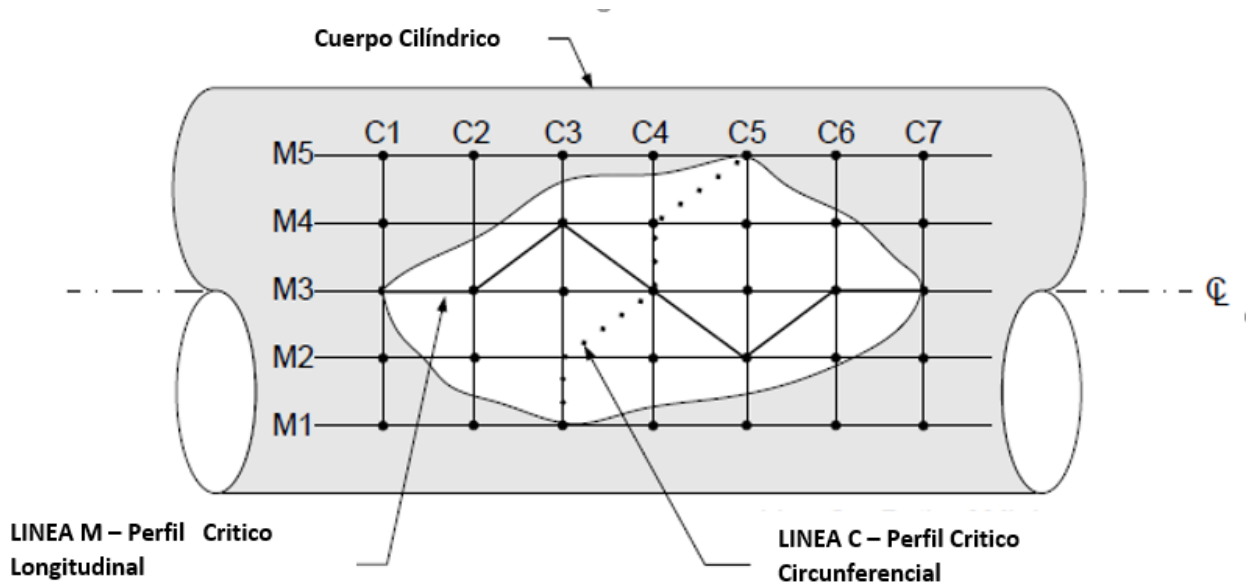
PLANO DE INSPECCIÓN Y PERFIL CRÍTICO DE ESPESORES
